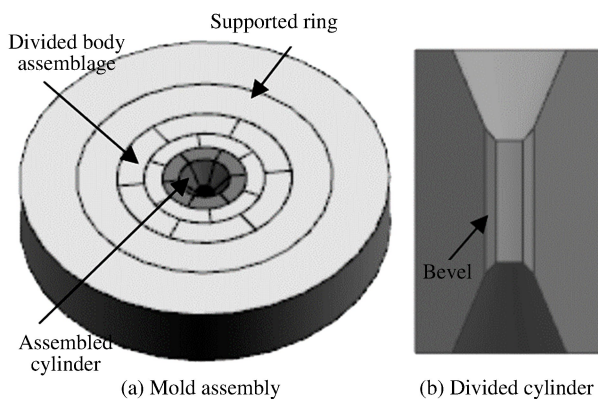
双斜边扇形块及双斜边扇形块式多层交错剖分模具示意图
